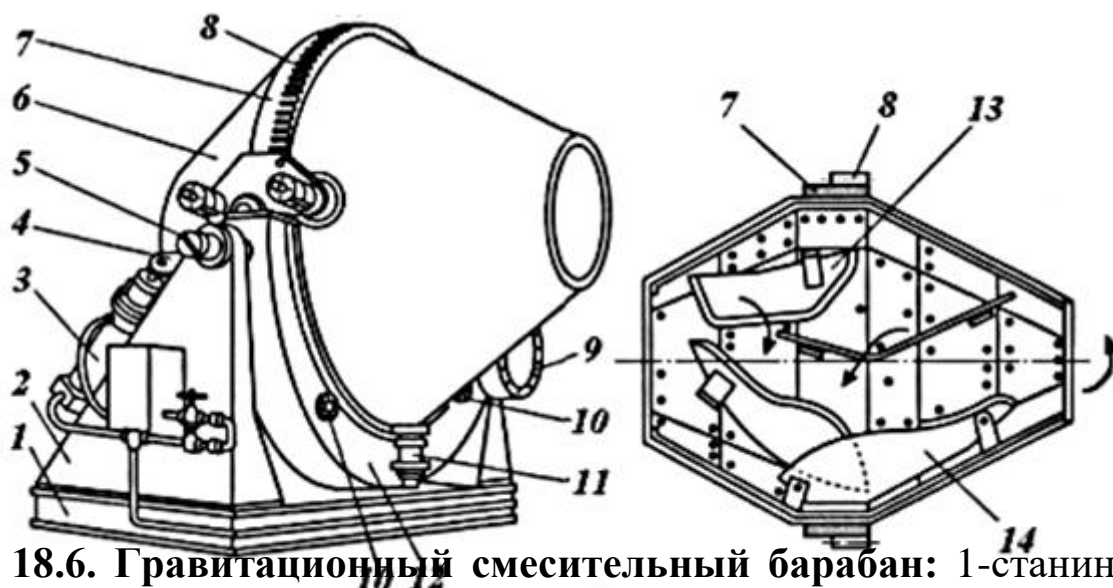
Гравитационный смесительный барабан: 1-станина; 2-стойка; 3-пневмоцилиндр наклона траверсы с барабаном; 4-кронштейн; 5-шип траверсы; 6-барабан; 7-обод; 8-зубчатый венец; 9-двигатель; 10-опорные ролики (сзади траверсы); 11-упорный ролик,
